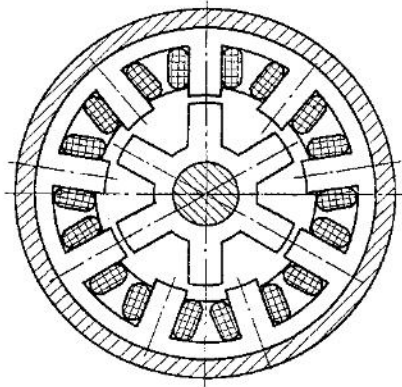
Розташування зубцевої обмотки якоря
